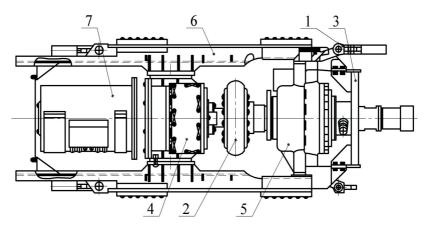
Головка бурового снаряда: 1 – ползун; 2 – шинно-зубчатая муфта; 3 – траверса; 4 – редуктор вращателя; 5 – опорный узел; 6 – каретка; 7 – электродвигатель
